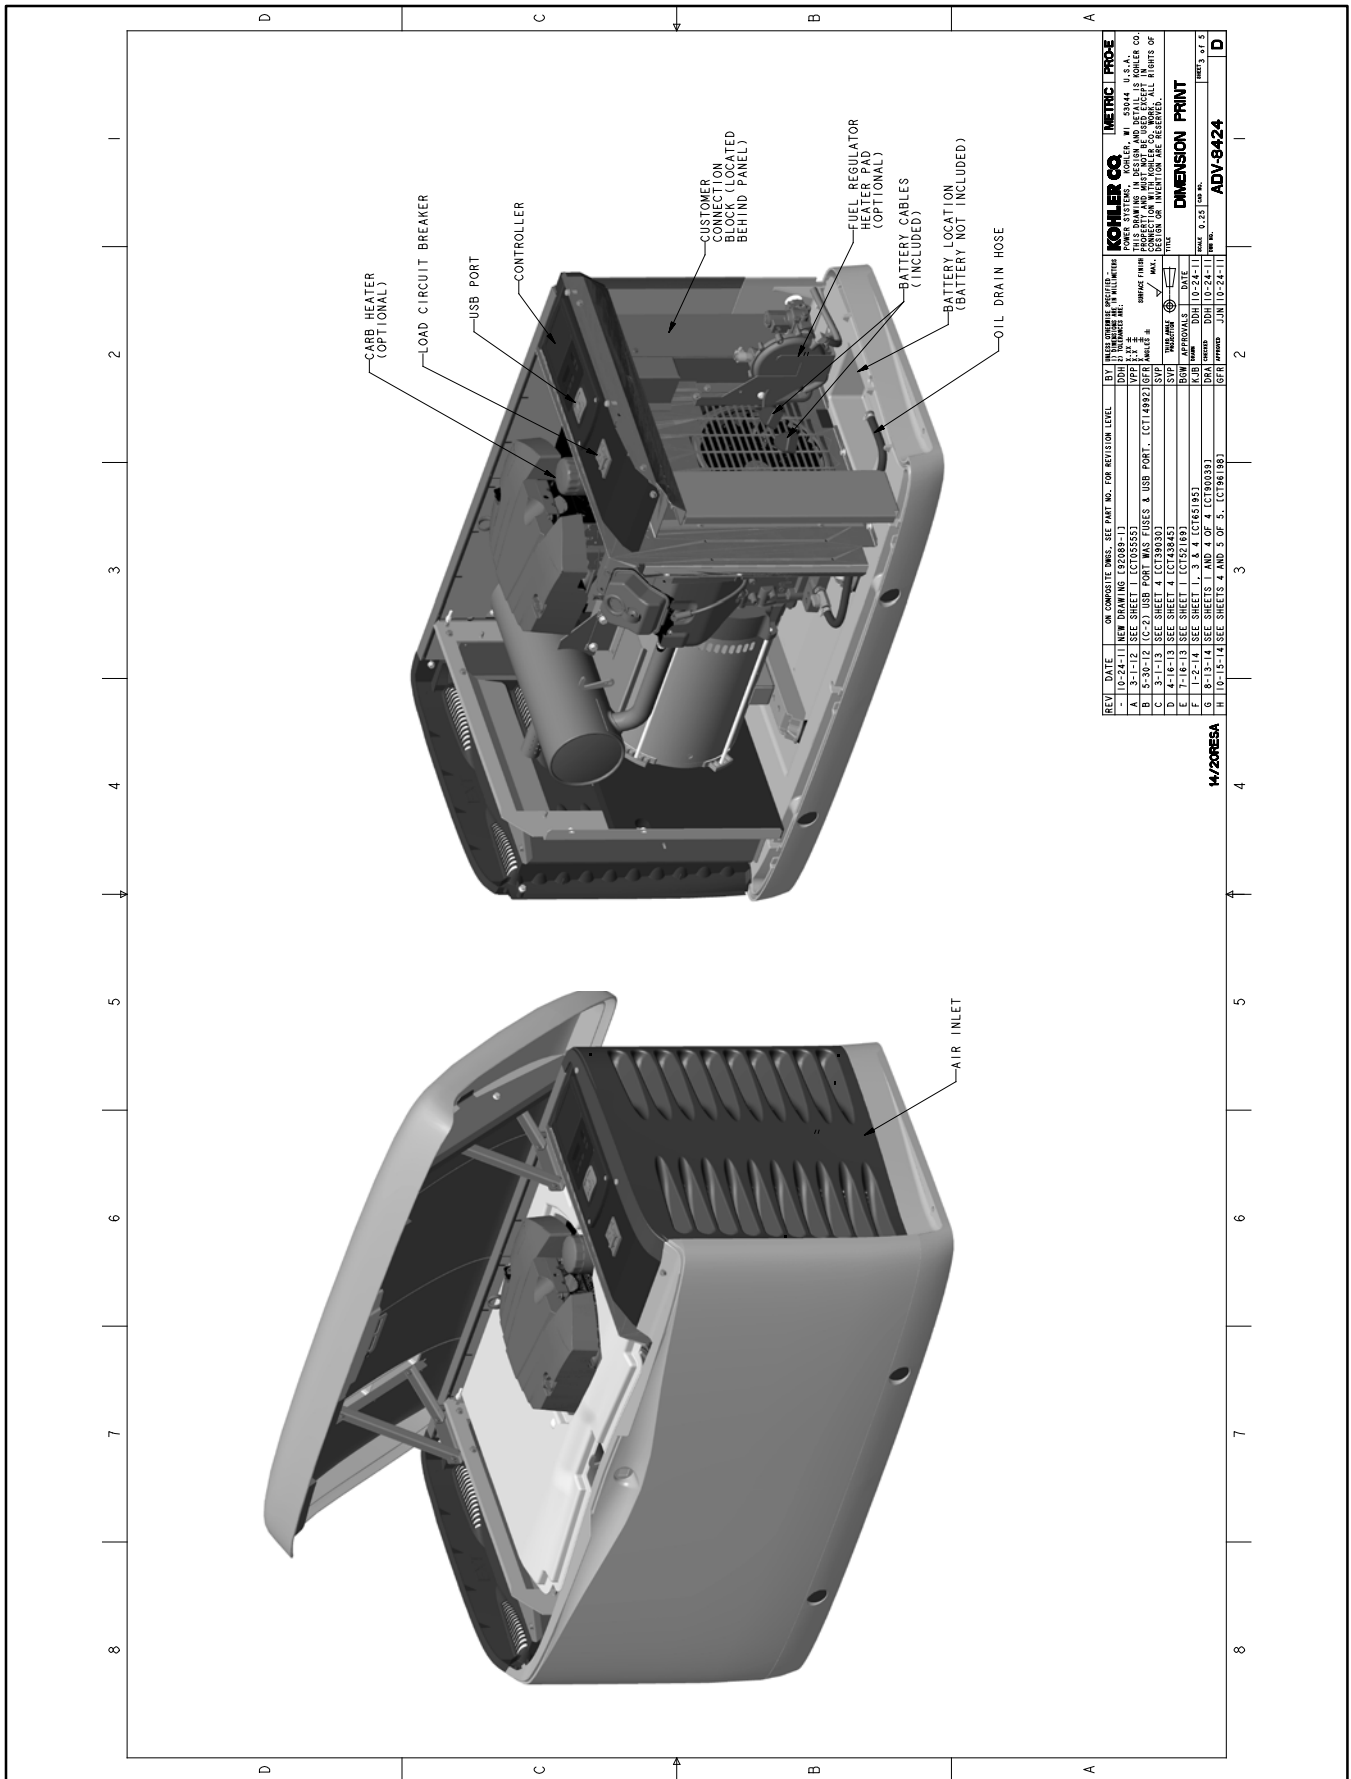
Размерный чертеж ADV-8424, лист 3 из 5
